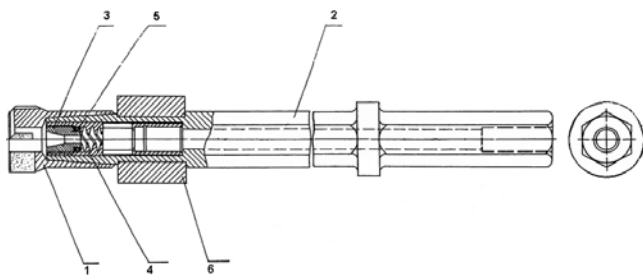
Квантово - механическая буровая штанга: 1 – коронка; 2 – корпус штанги; 3 – трубка Вентури; 4 – завихритель потока жидкости; 5 – пьезокерамический излучатель; 6 – резец для концентратора энергии
